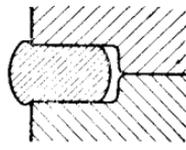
Обжатие заготовки в открытом заготовительном ручье недостаточной ширины
